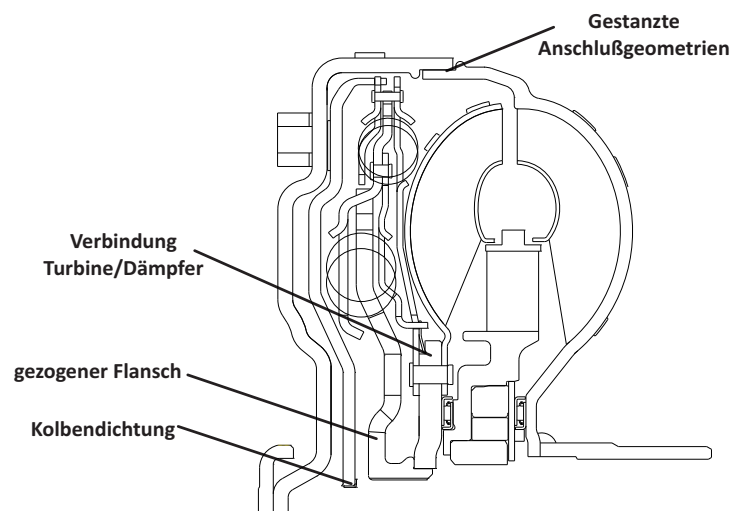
Wandlerquerschnitt mit vereinfachter Bearbeitung
